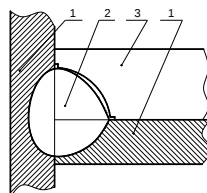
Схема контролю геометричних розмірів зварного шва за допомогою щупа
